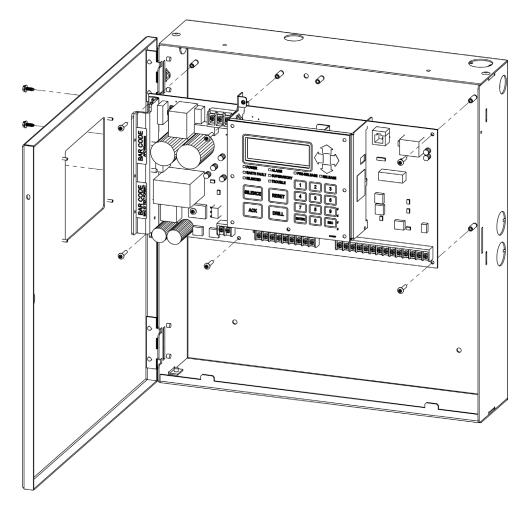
Gabinete IPA-60 mostrando montagem da placa de circuito
